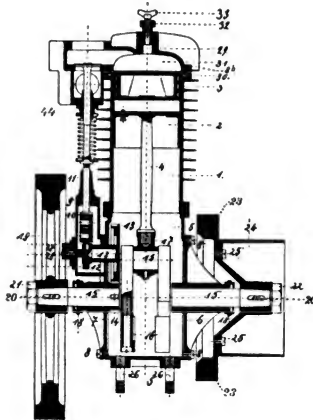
Motor der Maschinenfabrik „Cyklon“.
